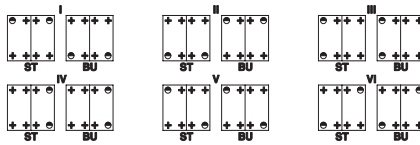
Механический ключ из болтов для корпусов с двумя контактными вставками
